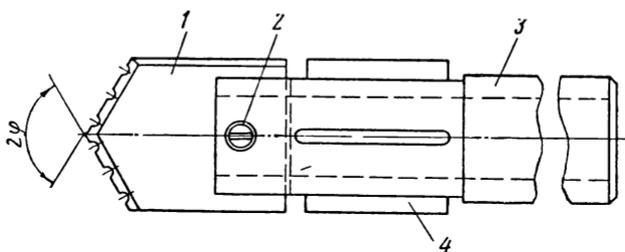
Перовое сверло с отверстиями для глубокого сверления
